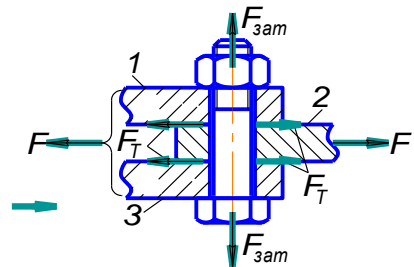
Схема встановлення болта в отвір деталі із зазором
